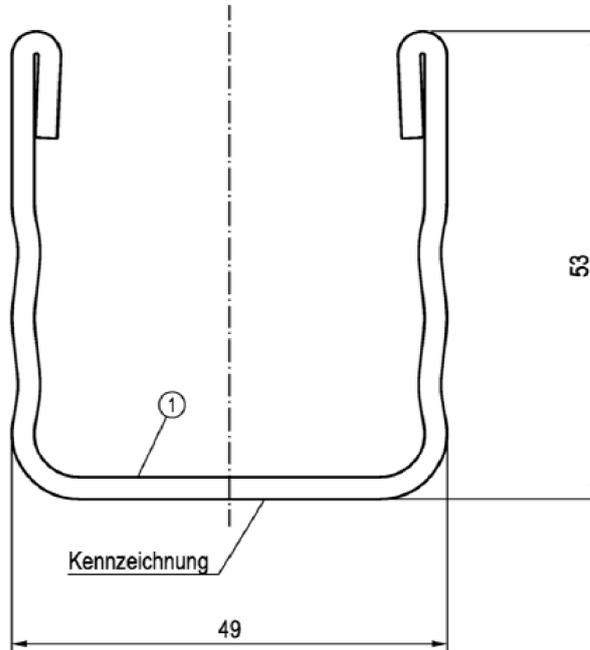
Details U-Alu Podesttreppe , Bauteile nach Z-8.1-16.2
